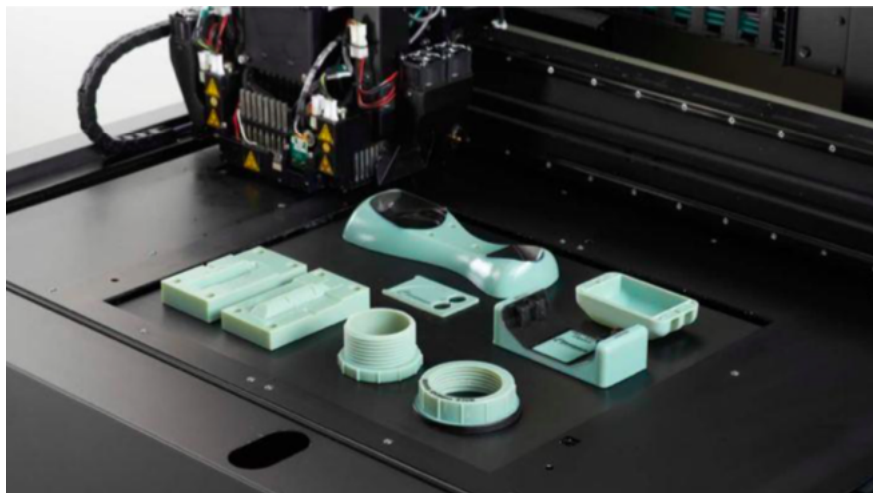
Piezas obtenidas mediante proceso de inyección de material [18].
